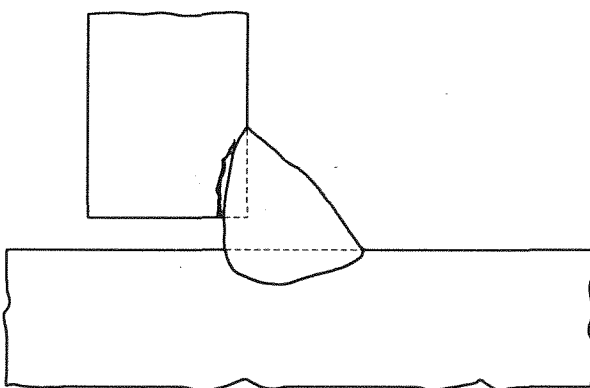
La concentración de tensiones en la raíz de la soldadura, en la entalla existente entre ella y el redondo, debido a la amplia separación redondo-pletina, puede originar grietas en la ZAC.
